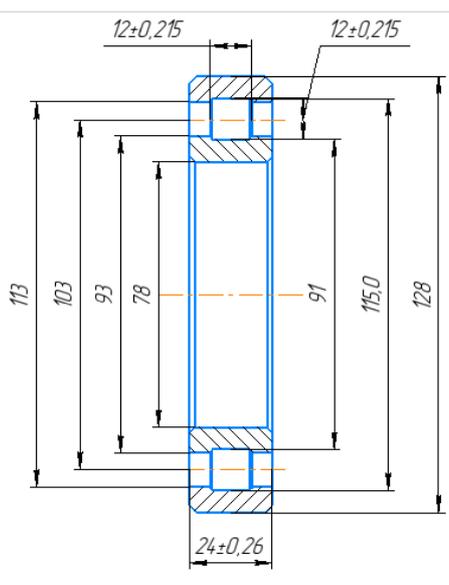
Вид тел поверхностей контакта тел и дорожек качения на поперечном сечении однорядного одноярусного бесепараторного подшипника: 1-внутренне кольцо; 2 – наружное кольцо; 3 - дорожка качения на наружном кольце; 4 - дорожка качения на внутреннем; 5-тела качения, имеющие погрешности вида «конусность»; контактирующие с внутренним кольцом
